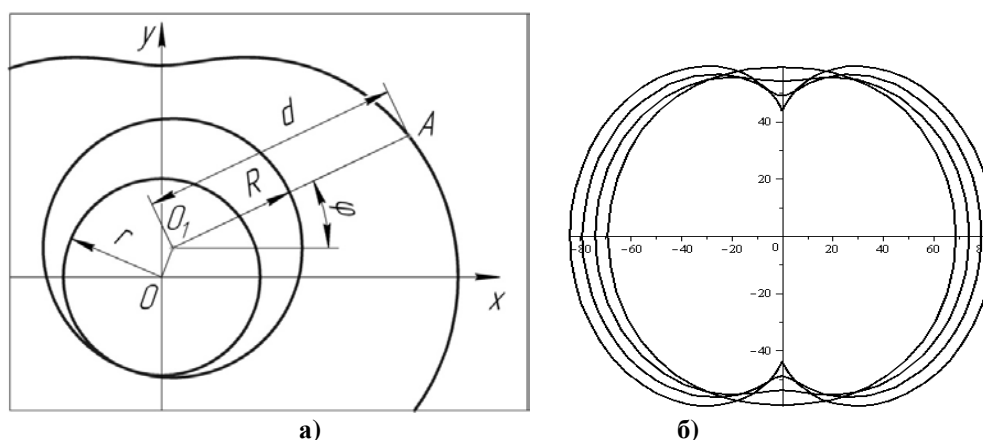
Формирование профиля корпуса компрессора: а – схема образования эпитрохоиды; б – семейство эпитрохонд для различных значений R при $R/r=3/2$.
